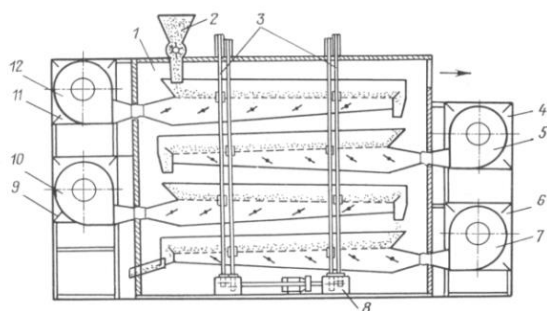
Вибросушильная установка АИ-КВО: 1 – сушильная камера; 2 – загрузочный бункер; 3 – вертикальные тяги; 4, 6, 9, 11 – паровые калориферы; 5, 7, 10, 12 – вентиляторы; 8 – эксцентриковый привод
